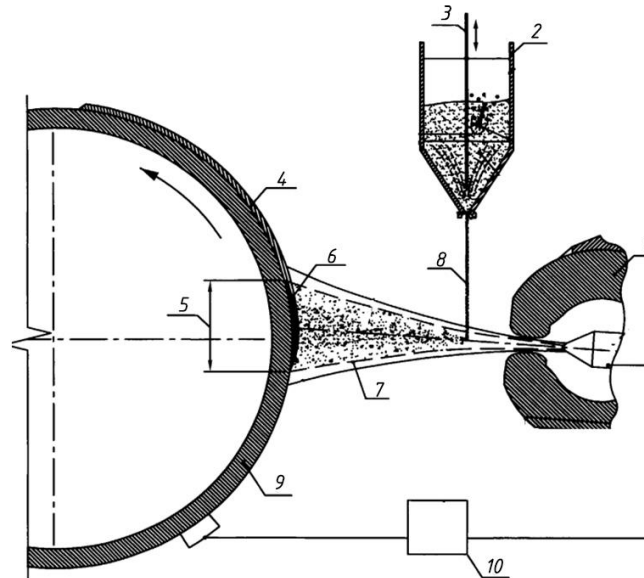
Общий вид автоматической установки для плазменно-порошковой наплавки
